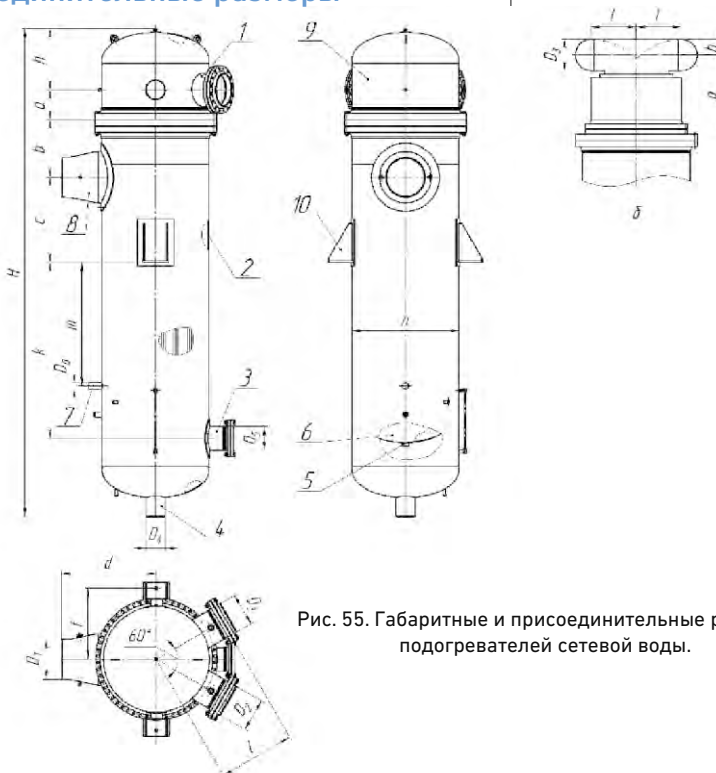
Габаритные и присоединительные размеры подогревателей сетевой воды.
